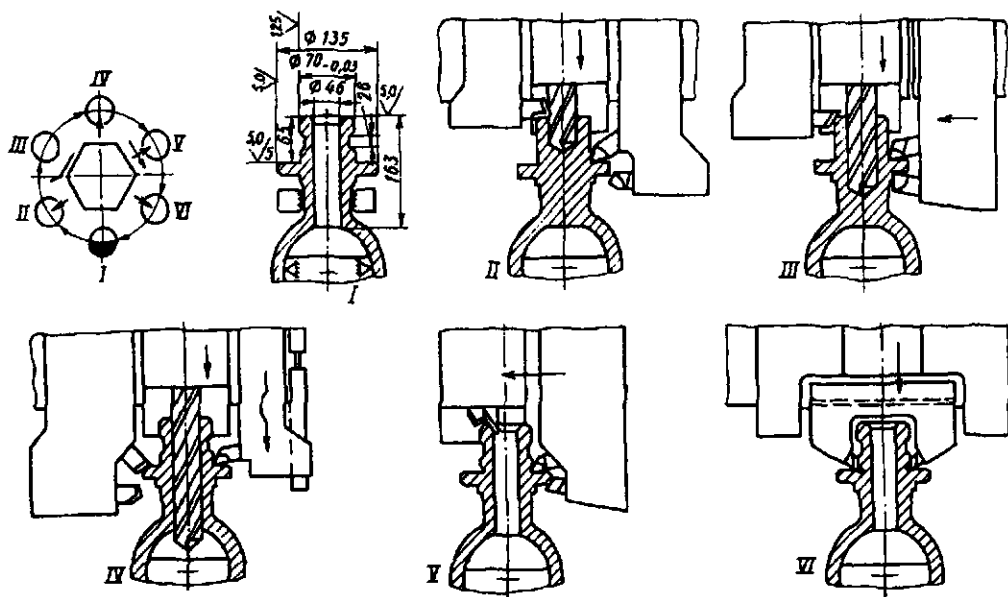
Наладка шестишпиндельного полуавтомата для полной обработки ступицы шаровой опоры
